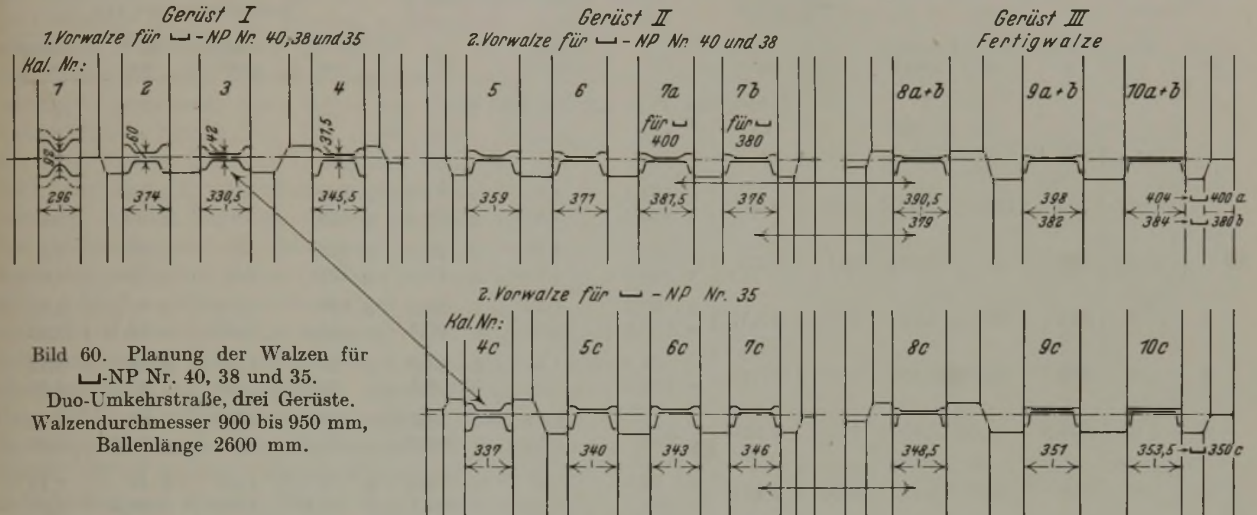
Planung der Walzen für \perp -NP Nr. 40, 38 und 35. Duo-Umkehrstraße, drei Gerüste. Walzendurchmesser 900 bis 950 mm, Ballenlänge 2600 mm.
